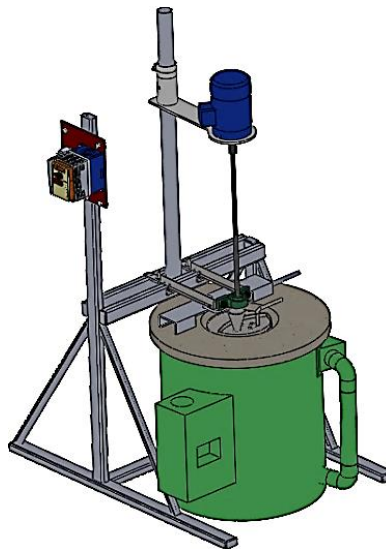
Montaje del diseño del equipo stir casting en el horno de fundición.
